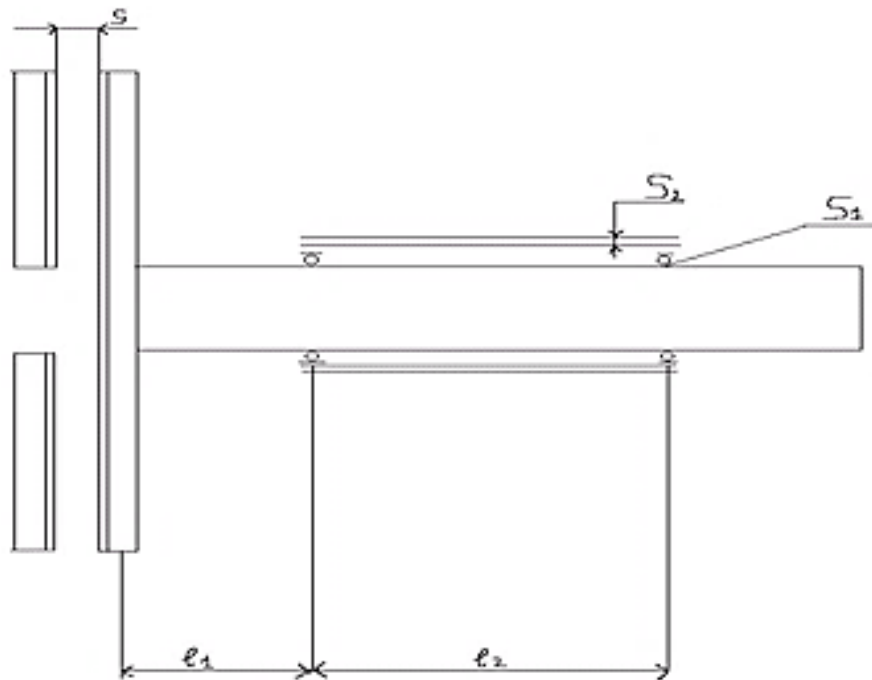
Расчетная схема для расчета биений ротора: S – межножевой зазор; S_1 – радиальный зазор подшипников; S_2 – зазор между стаканом ротора и корпуса
